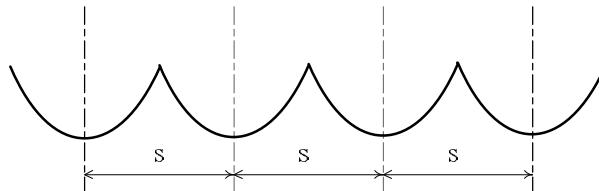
Вид профиля шероховатости поверхности плоской детали после обработки ШСУ
